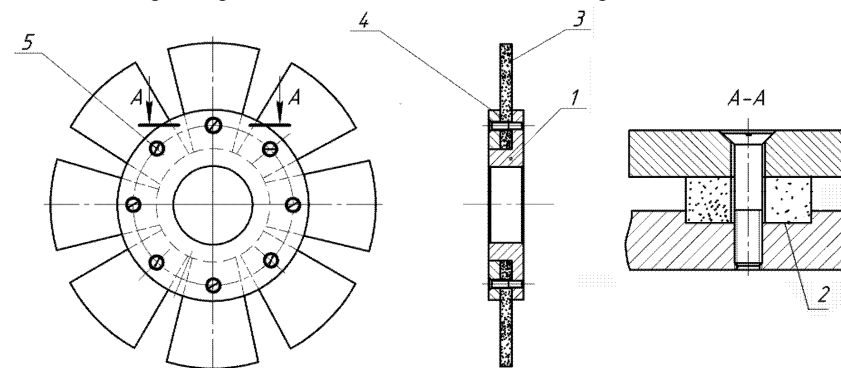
Конструкція перервного, збірного абразивного круга для загострювання зубців рамних пилок
